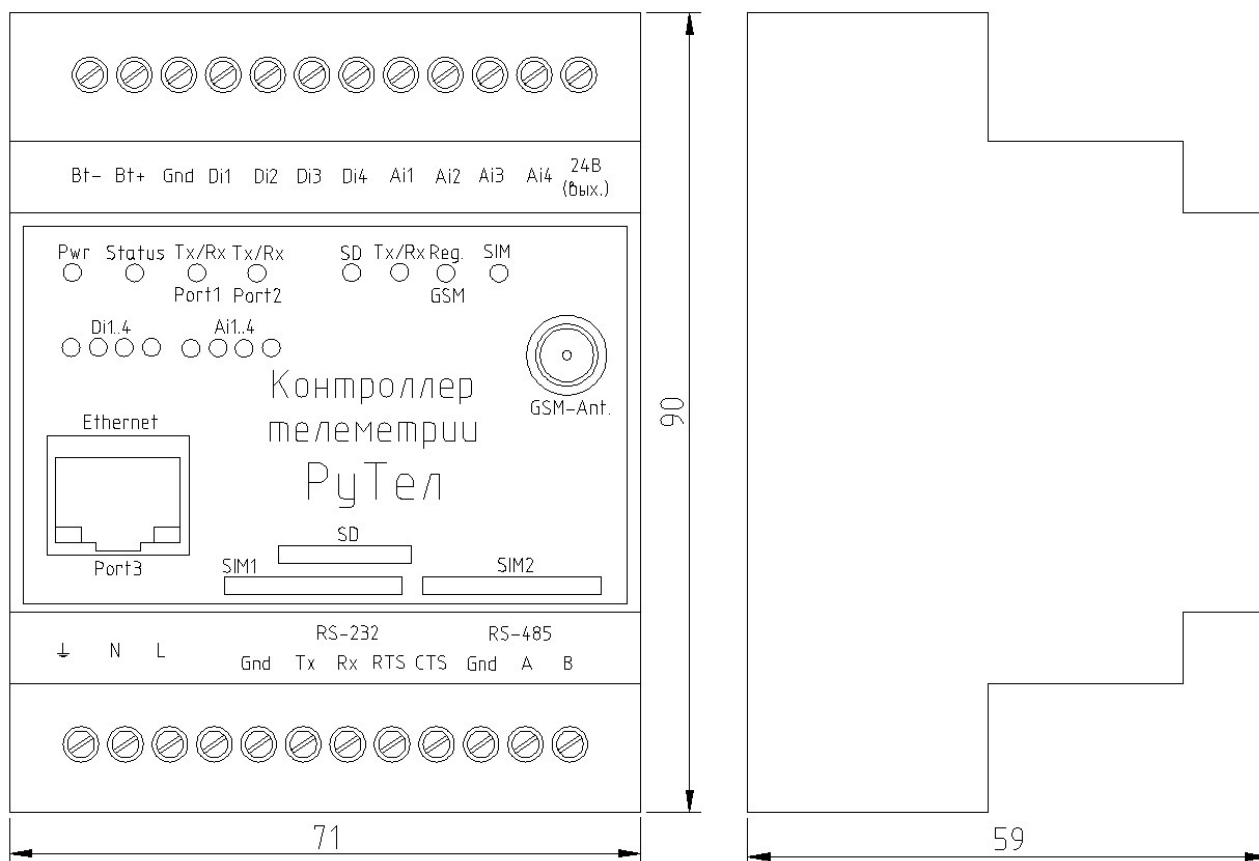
Эскиз контроллера «РуТел» с габаритными размерами
